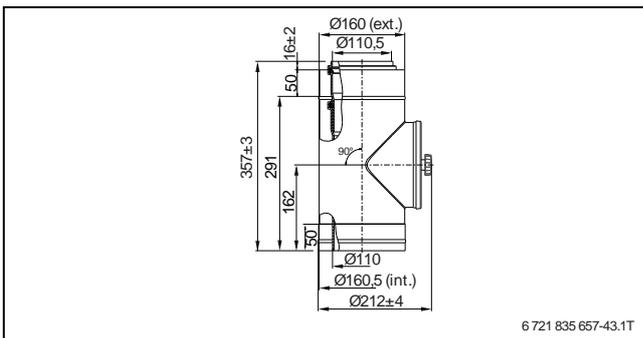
Konzentrisches Rohr mit Prüföffnung (Maße in mm)
